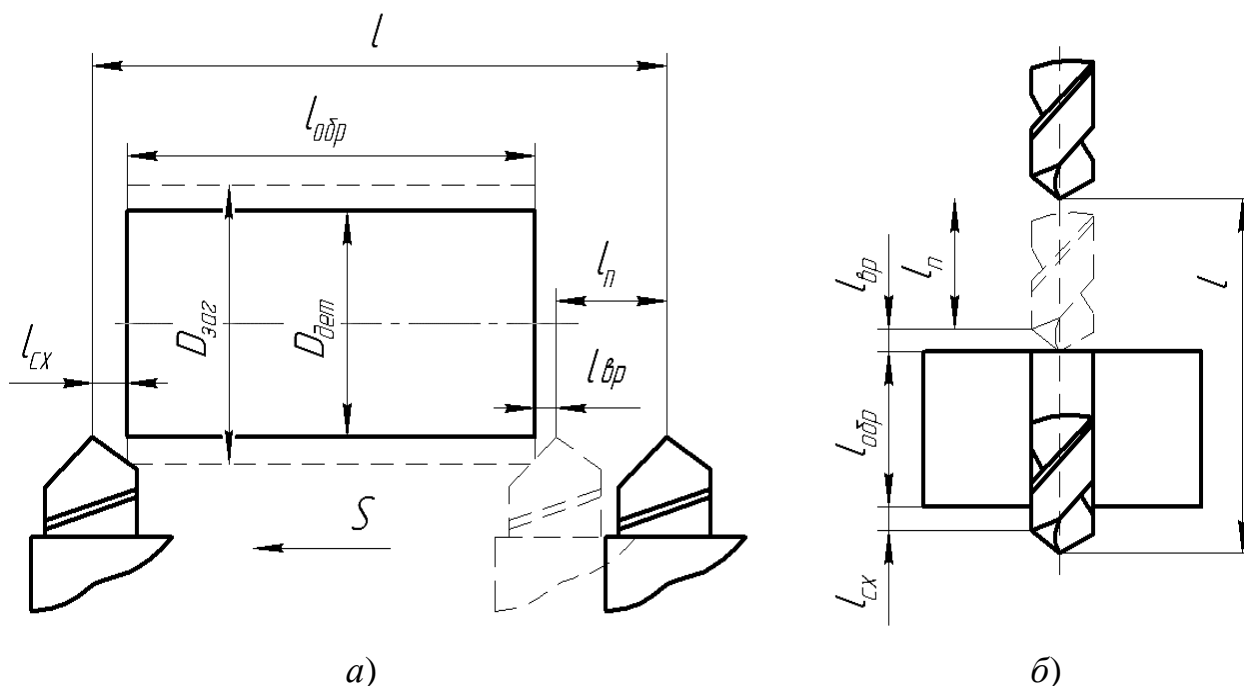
Схеми для визначення розрахункової довжини оброблення
